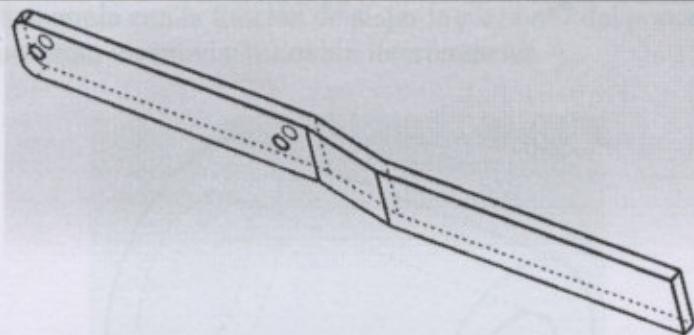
Brazo accionamiento mordaza. Plano EM-004.
